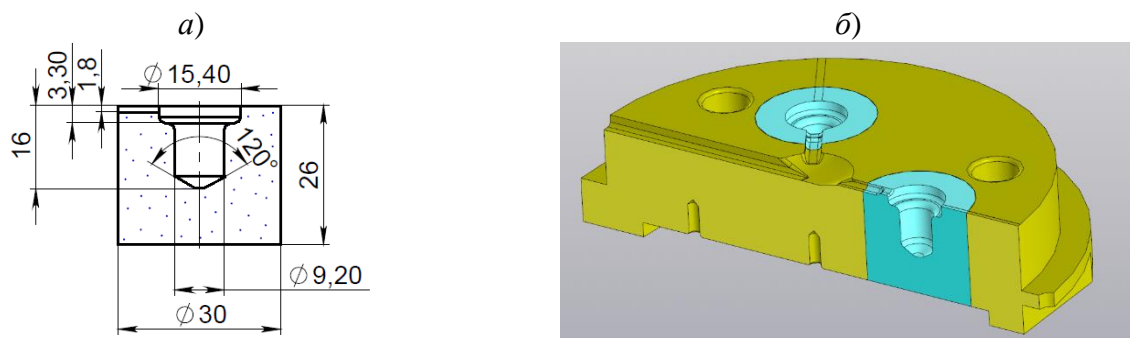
Деталь "вкладыш" (а) и элемент пресс-формы (б) для получения пластмассовых изделий
